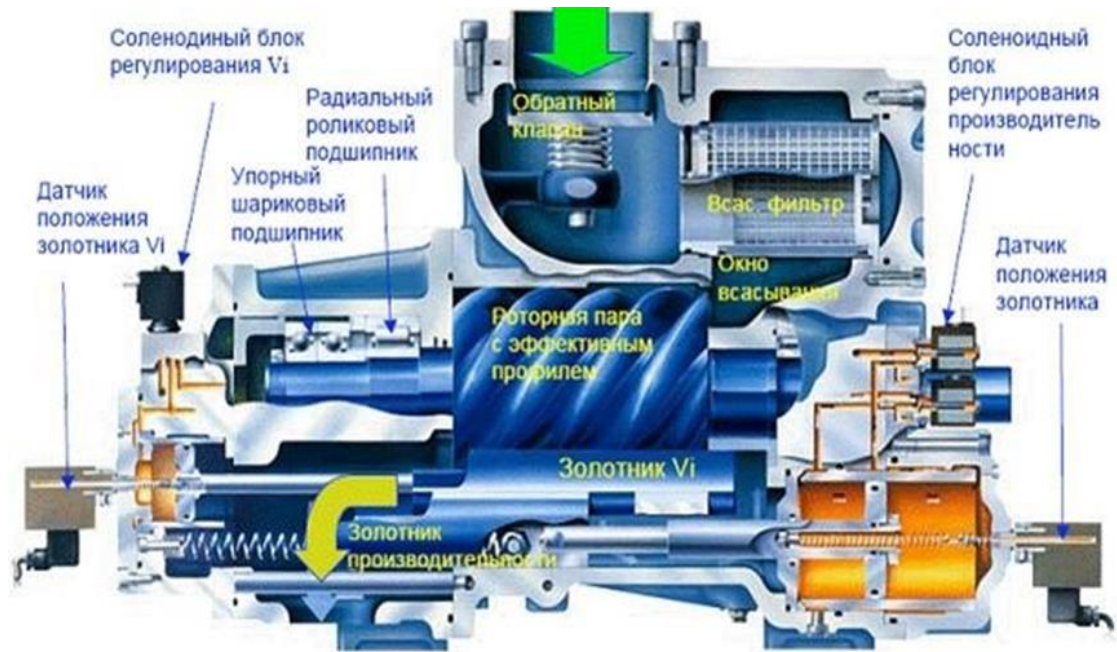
Схема винтового компрессора Винтовые компрессоры бывают безмаслянные и маслозаполненные
